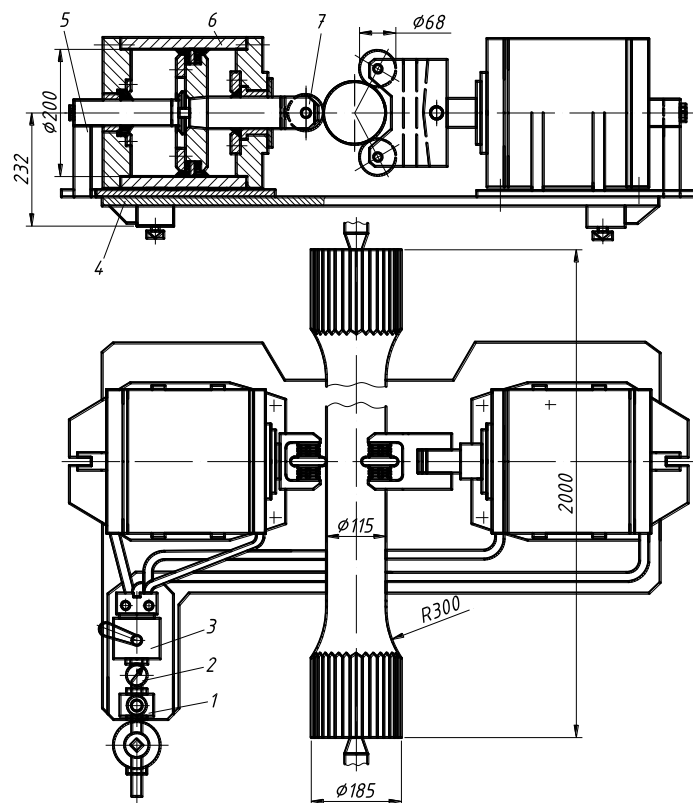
Приспособление для обкатывания торсионов исчезающих упоров прокатных станов
